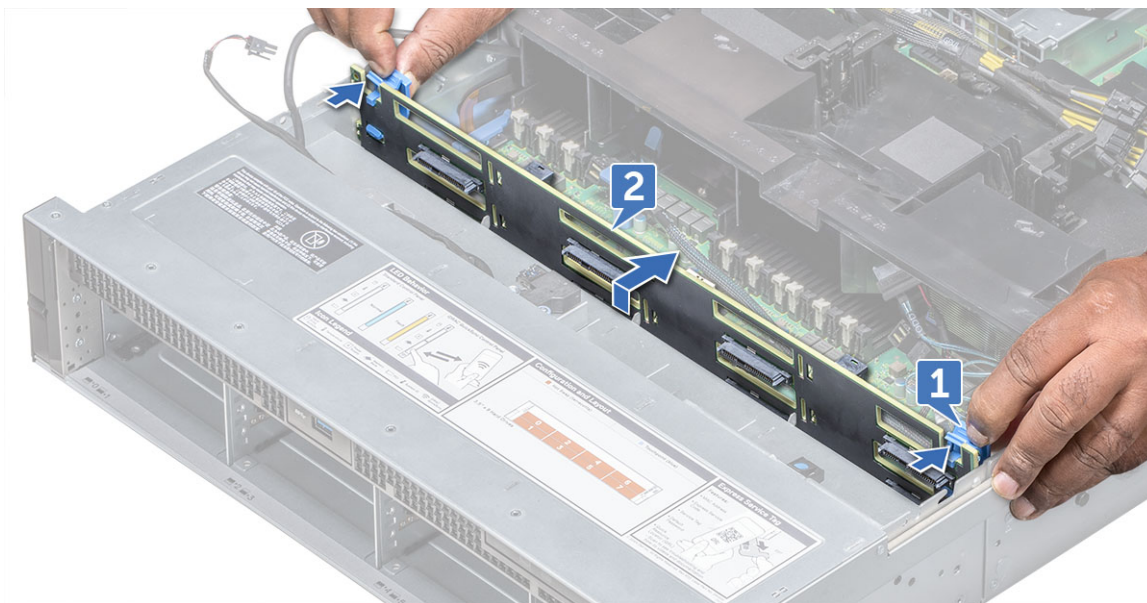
Desmontaje del plano posterior de la unidad de disco duro
